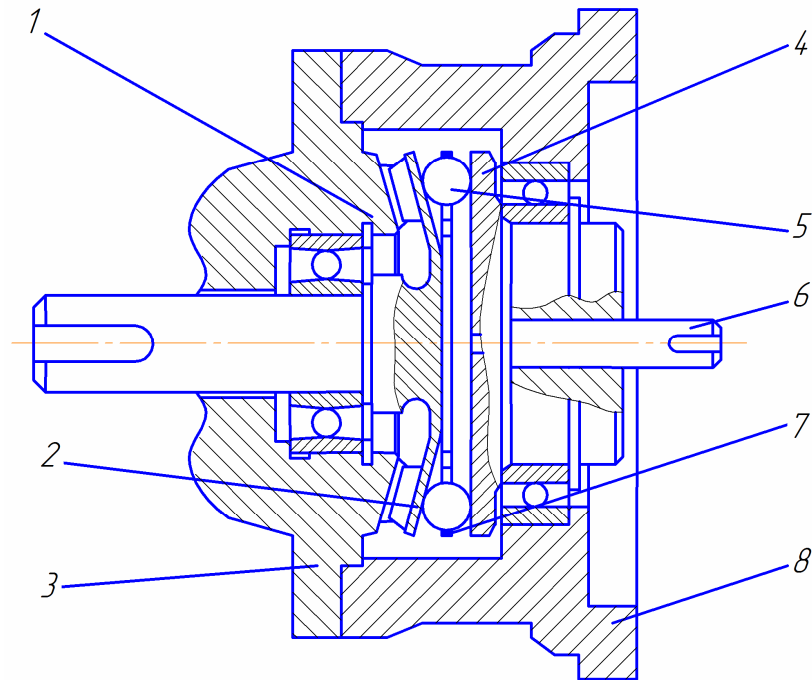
Конструктивная схема торцевой волновой зубчатой передачи: 1 - жесткое колесо, 2 – гибкое колесо, 3 - крышка, 4 - диск генератора волн, 5 – шарики, 6 - входной вал, 7 - сепаратор, 8 – корпус
